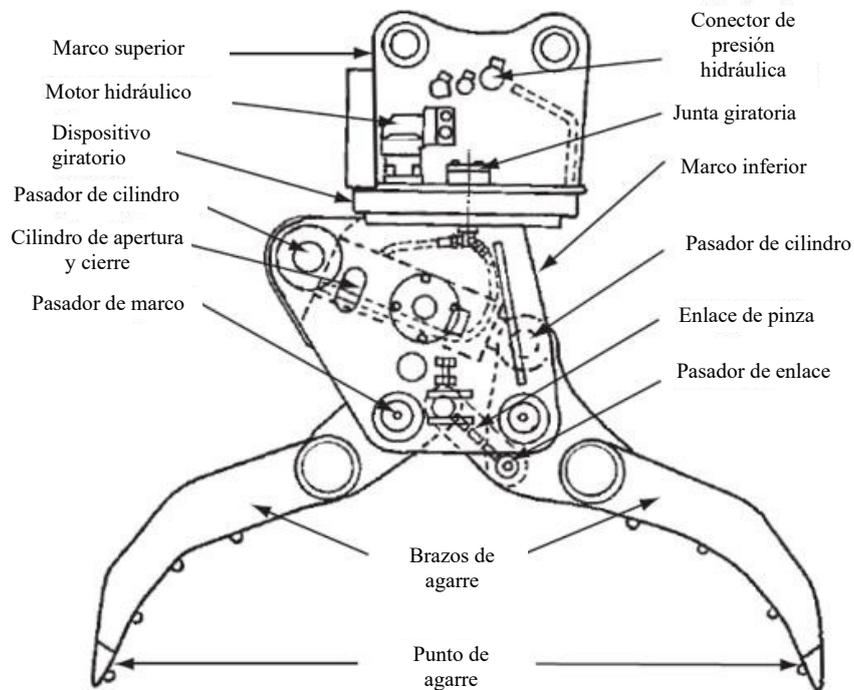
Nombres de cada parte de una herramienta de agarre (con dispositivo de giro, tipo accionada por cilindro interno)
